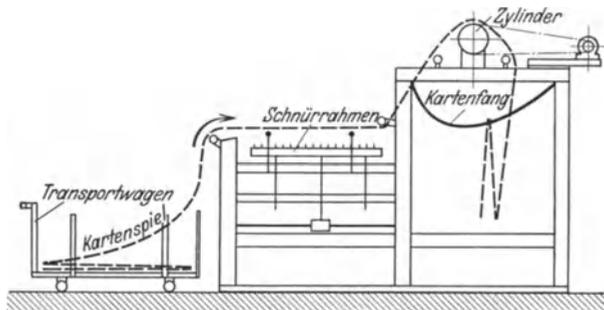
Schema einer Karten-Reparatur-Maschine.
